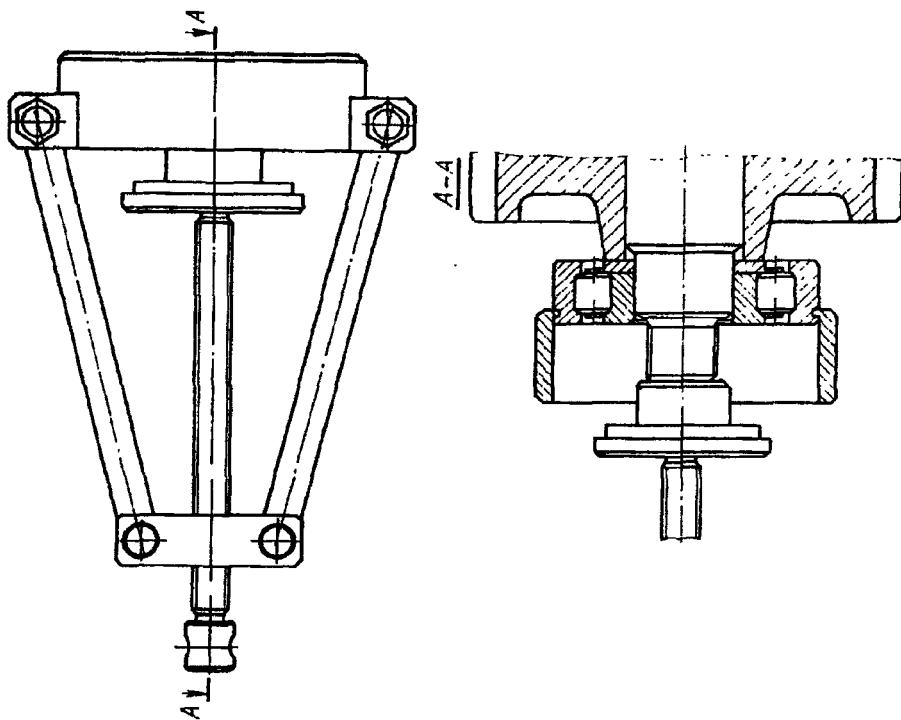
Снятие внутреннего кольца переднего подшипника промежуточного вала
